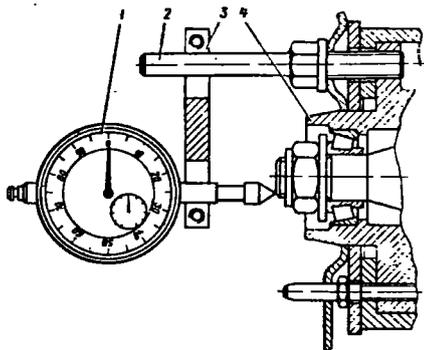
Проверка осевого зазора подшипников ступицы переднего колеса приспособлением 02.7834.9505: 1 - индикатор; 2 - болт; 3 - кронштейн; 4 - ступица
